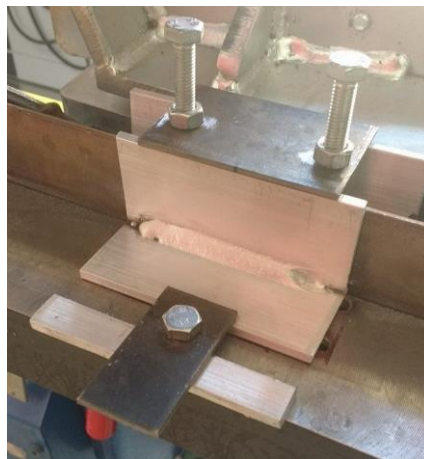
Exemplo de junta soldada durante os experimentos.
